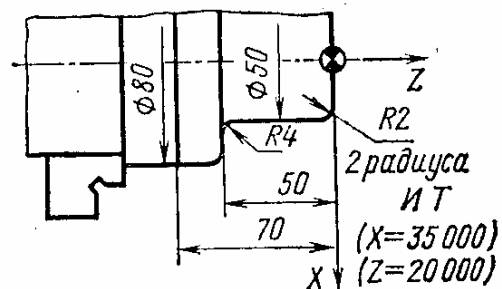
Эскиз заготовки (к заданию 16.10)
